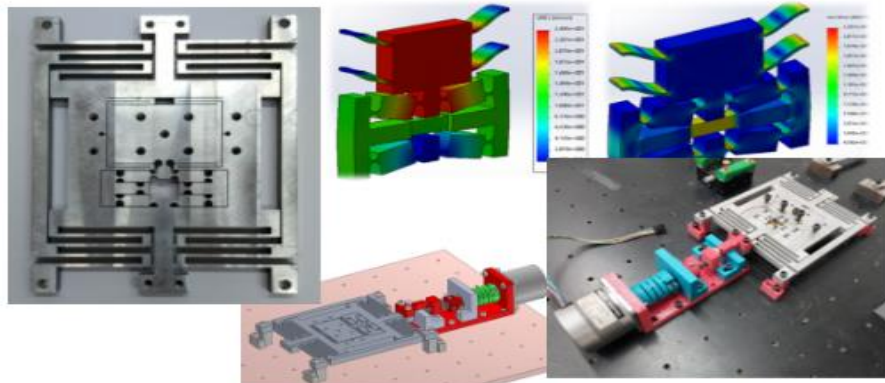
Diseño y montaje del posicionador dual de alta resolución.
